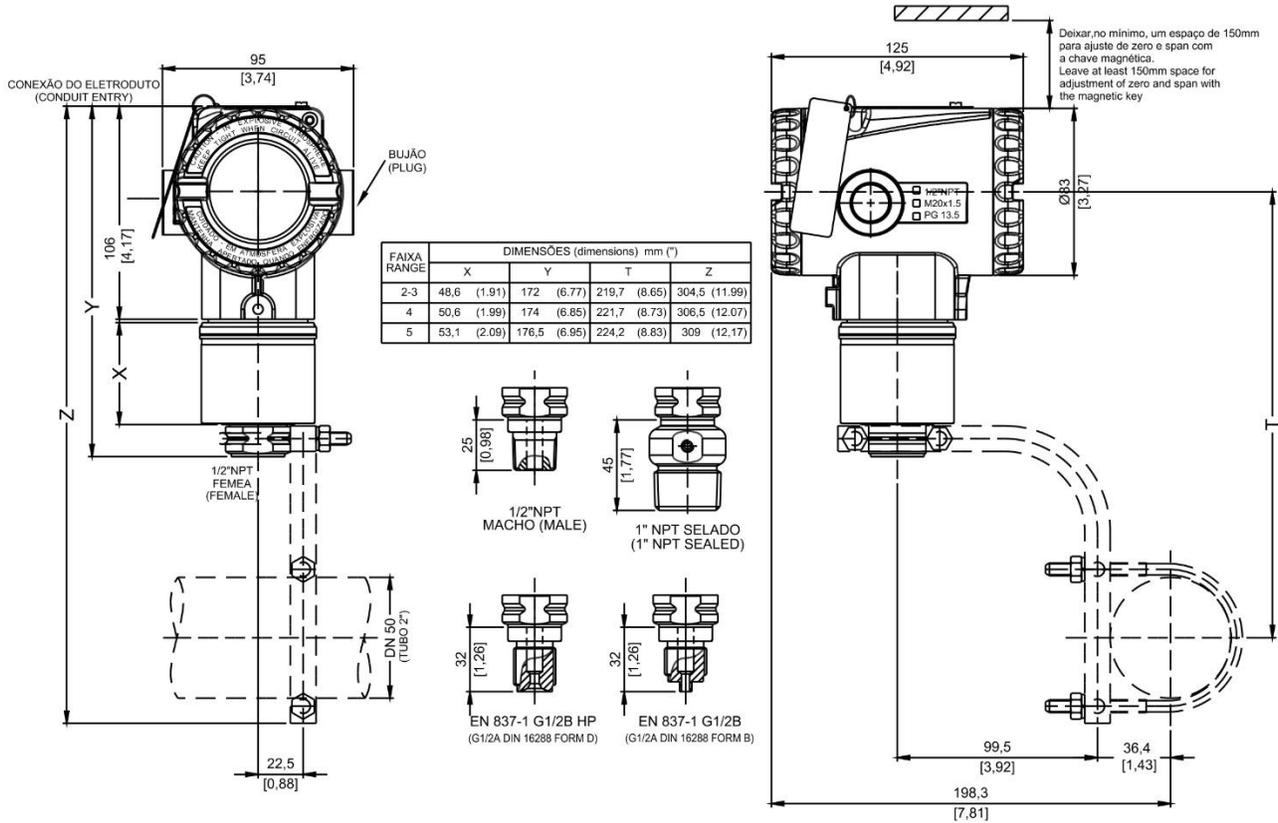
(f) – Desenho Dimensional de Montagem do LD400 HART - Transmissor Manométrico G INLINE
